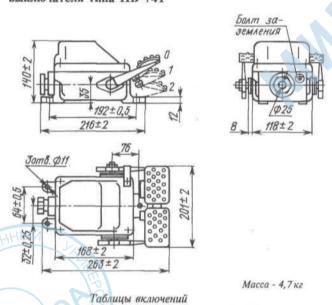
Габаритные, установочные размеры и масса выключателя типа НБ-742
